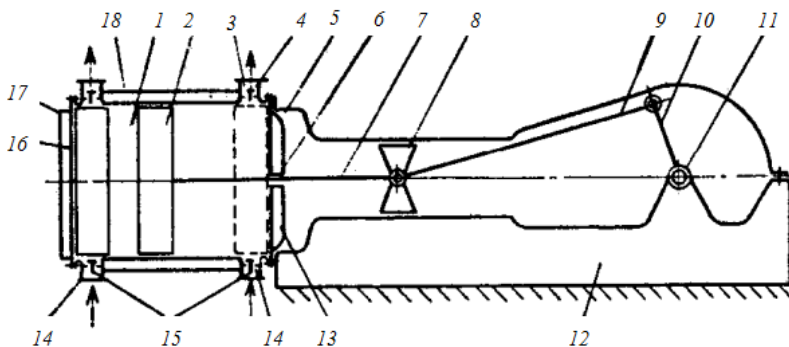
Схема горизонтального одноступенчатого компрессора двойного действия:
